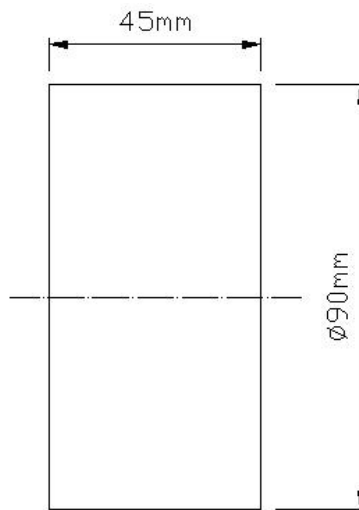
2. Dimensiones del tocho para fabricar el pistón de la prensa neumática. Fuente: Los Autores.
